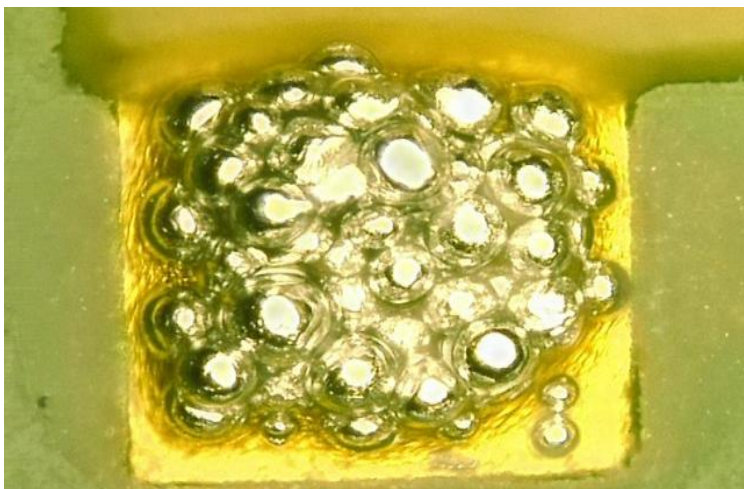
Impresión de soldadura de pasta usando soldadura tipo IV
